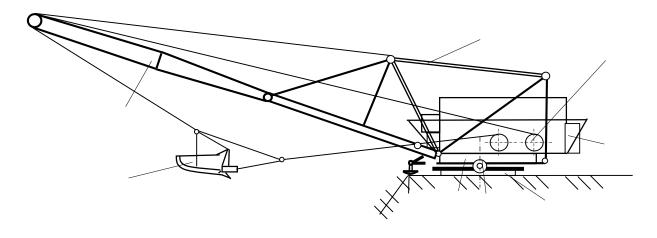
Схема одноковшового экскаватора 1 — база; 2 - поворотная платформа; 3 — стрела; 4 — ковш (драглайн); 5 - противовес; 6 — тяговые лебедки; 7 — подвес стрелы; 8 - механизм шагания; 9 — подпятник
